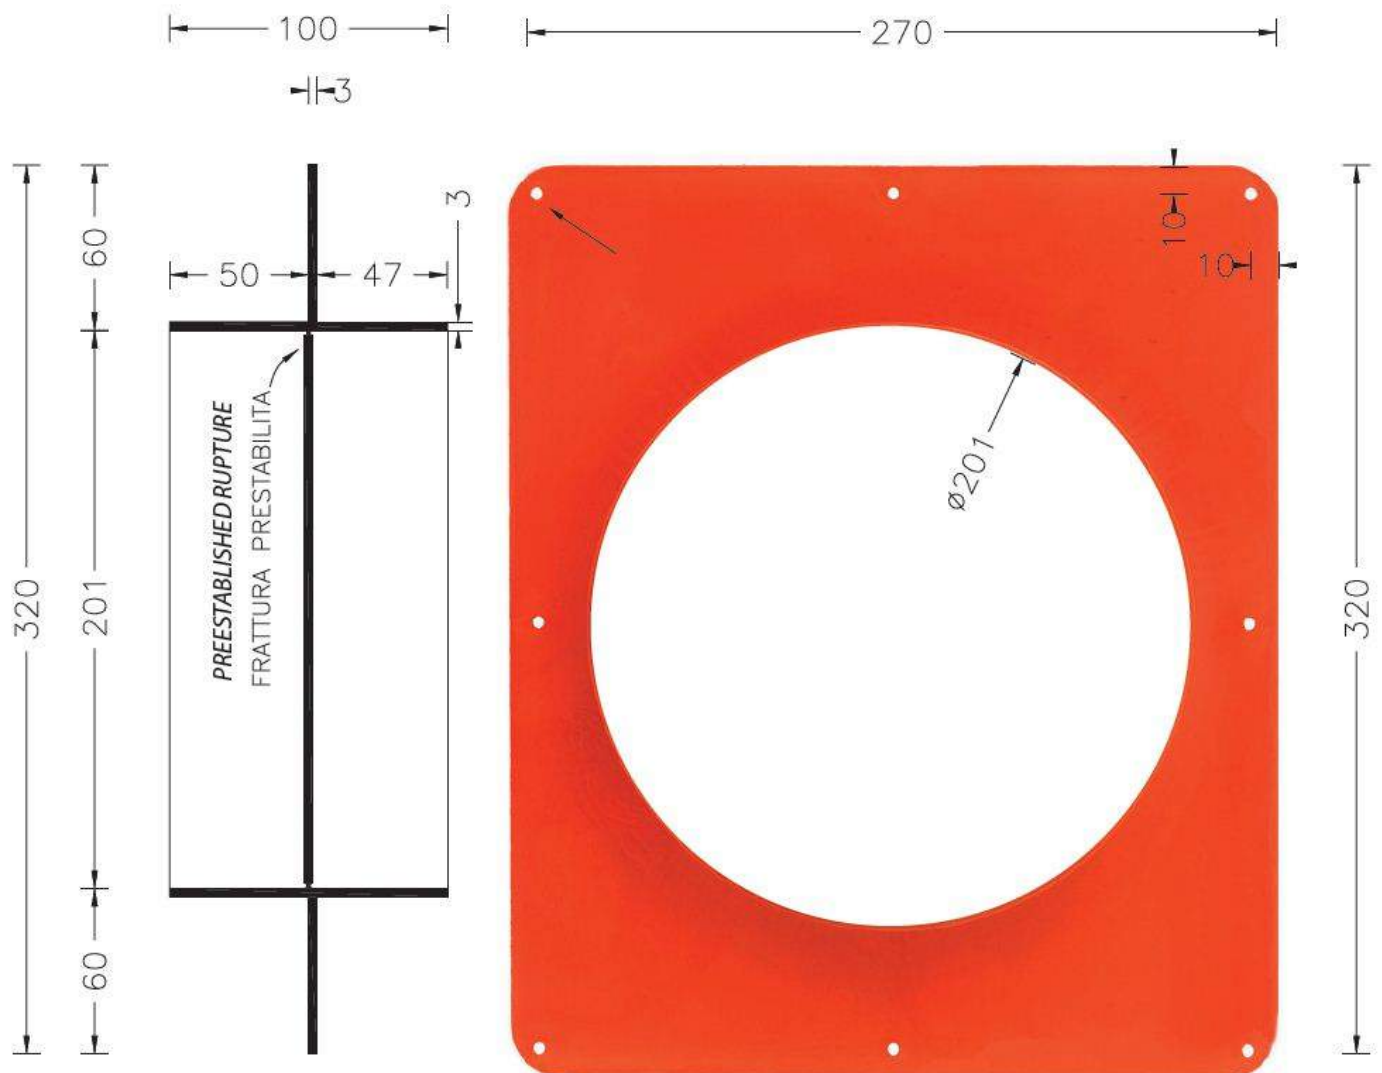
prospetto e sezione flangia a rottura prestabilita
